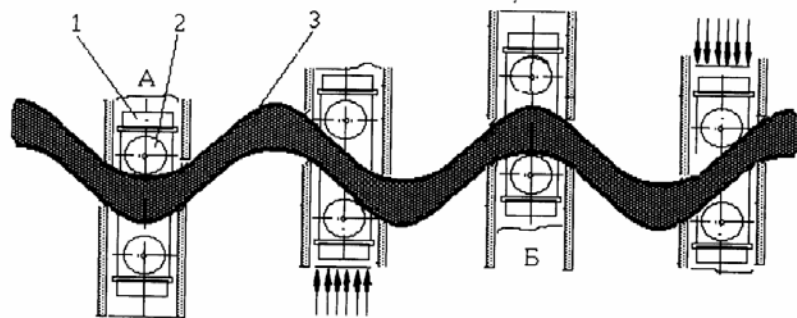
Схематическое изображение в виде развертки реверсивного аксиально-поршневого пневматического двигателя
